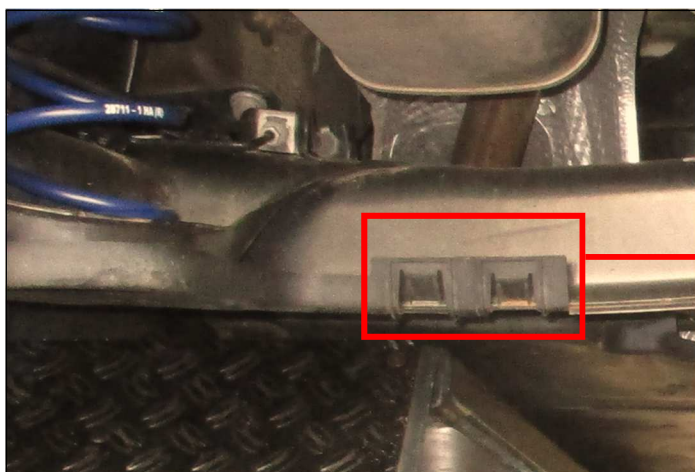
& 6: Ausklinken des Steinschlagschutzes (fahrzeuginnere Klemmbefestigung wird entfernt)
